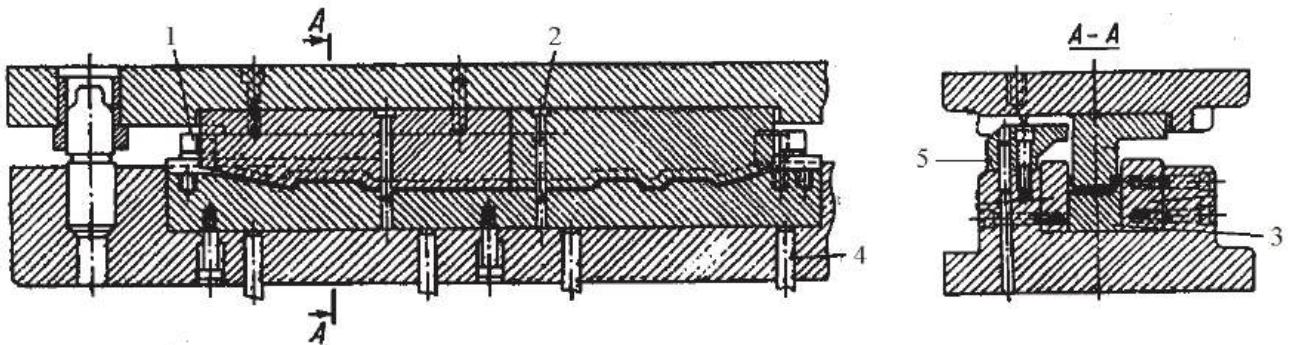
Штмп для формування підсилювальної накладки під навішування [13]
